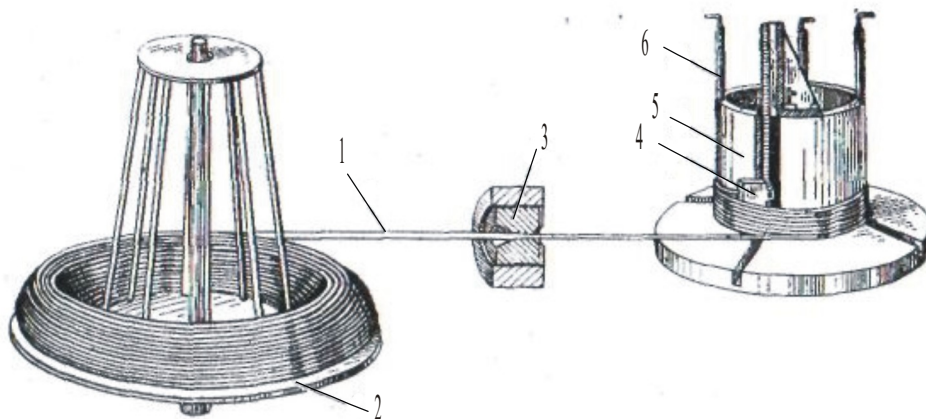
Принцип однократного волочіння: 1 - дріт; 2 - розмоточна фігурка; 3 - волока; 4 - кліщі; 5 - барабан; 6 - спиця
